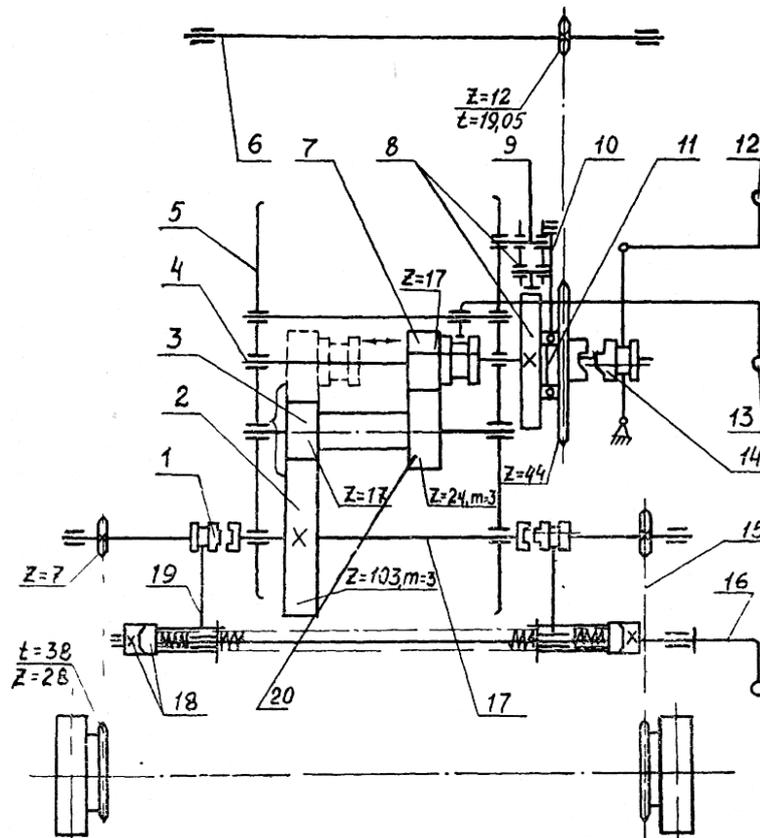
Кинематическая схема механизма передвижения: 1 - муфта кулачковая; 2 - колесо зубчатое; 3 - блок зубчатый; 4 - вал привода; 5 - редуктор; 6 - эксцентриковый вал; 7 - шестерня; 8 - храповой механизм; 9 - каретка; 10 - шатун; 11 - эксцентрик; 12 - рукоятка транспортной скорости; 13 - рукоятка реверса; 14 - полумуфта; 15 - цепная передача на ходовые колеса; 16 - вал управления; 17 - вал; 18 - кулачки; 19 - вилка; 20 - шестерня
